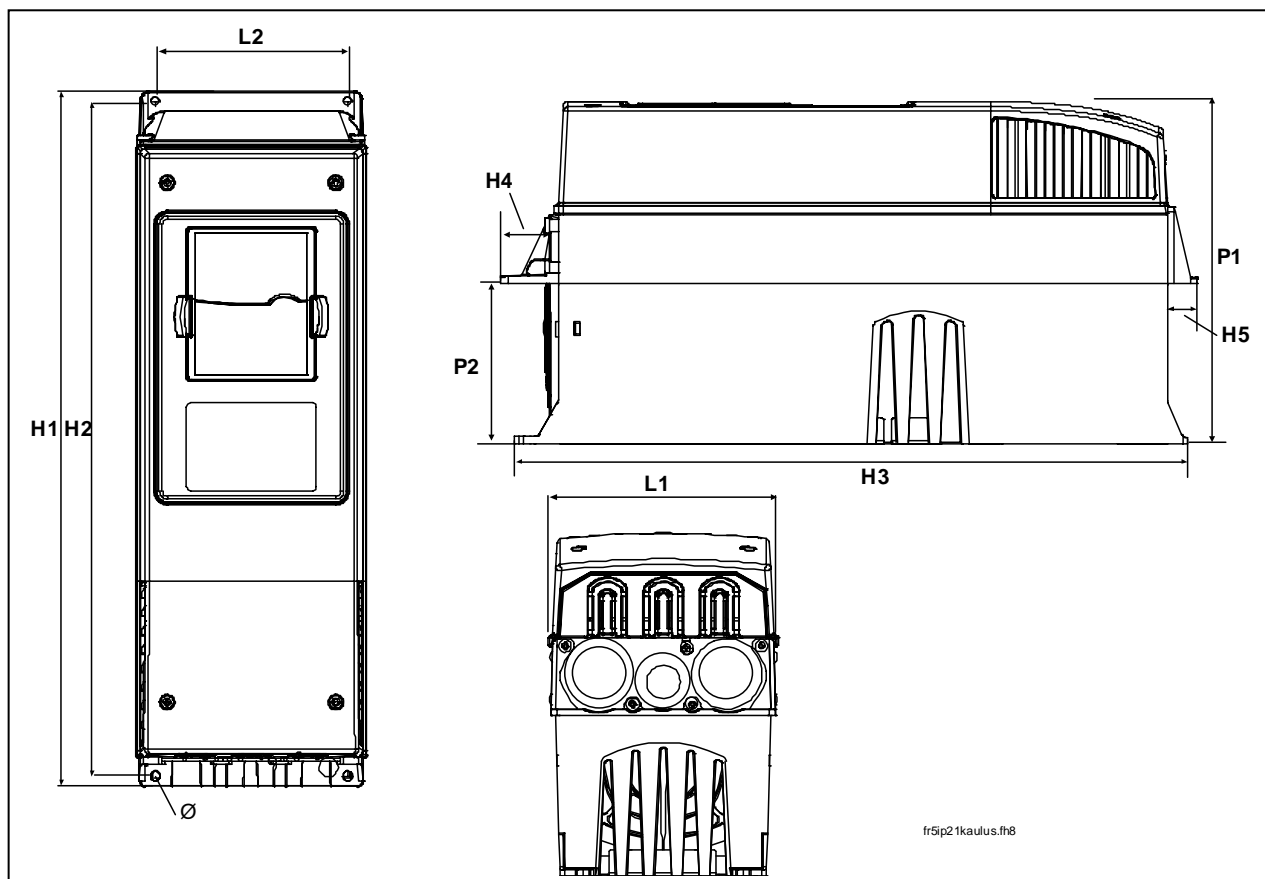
Dimensioni di ingombro del Vacon NX\_, montaggio a flangia da FR4 a FR6
